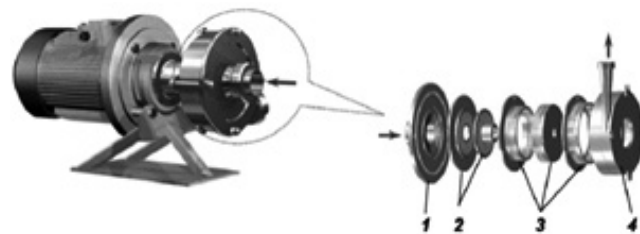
Корпусний роторно-пульсаційний апарат з дисковими елементами [37]: 1 — кришка; 2 — статорно-роторний дисковий вузол; 3 — статорно-роторний циліндричний вузол; 4 — корпус з вихідним патрубком
